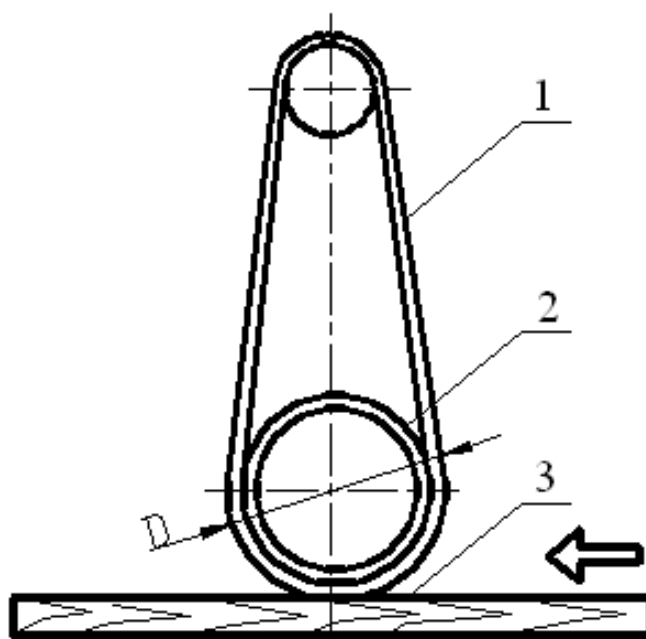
Широколенточный шлифовальный станок с верхним расположением агрегата:
